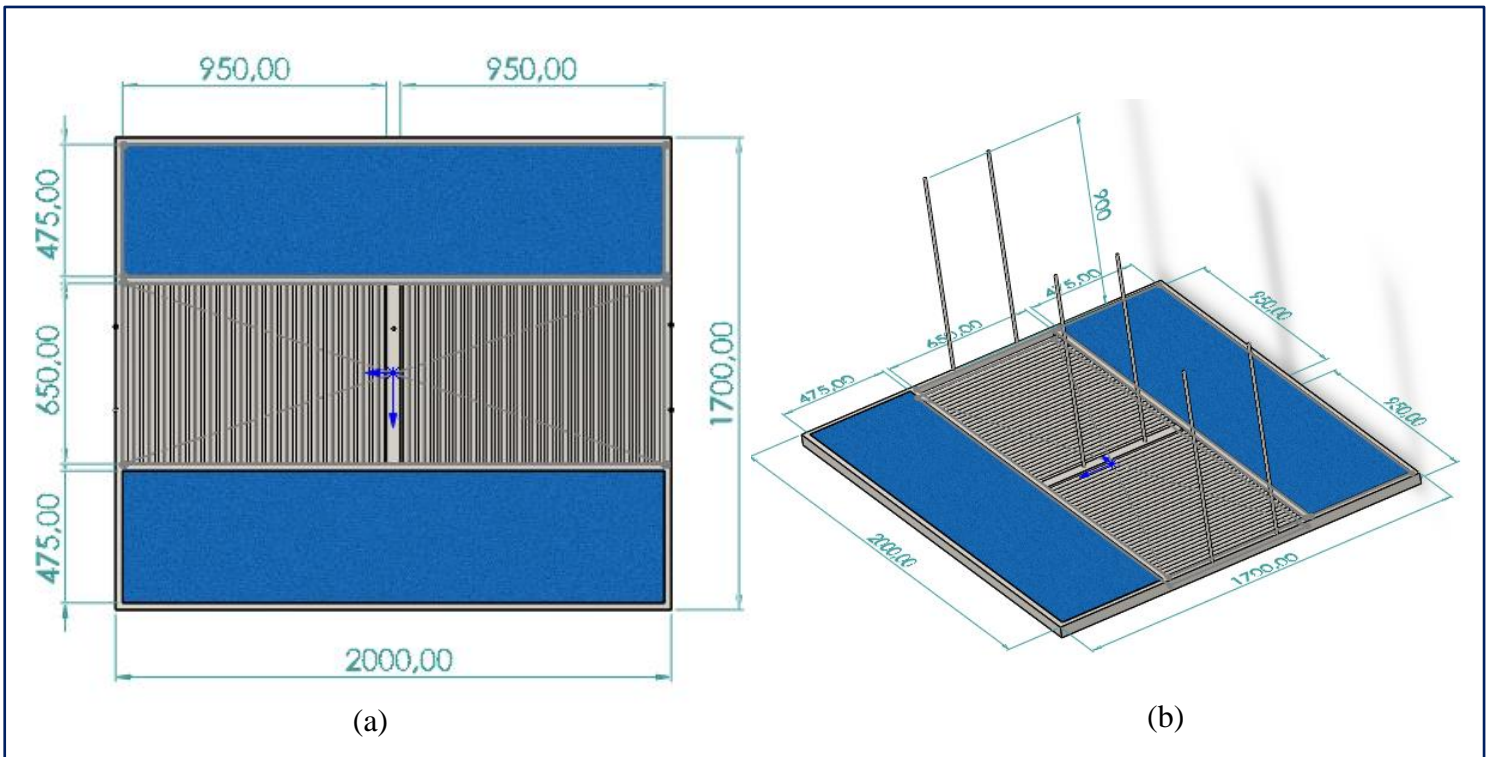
Dimensões do Protótipo - Vista Superior e Perspectiva
